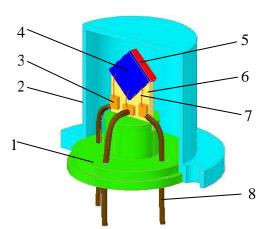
Конструкция герметизированного модуля для регистрации тепловых нейтронов, где 1 — металлическое основание; 2 — металлический корпус; 3 — промежуточный вывод; 4 — ПКД; 5 — гадолиниевый конвертер; 6 — диэлектрический держатель детектора; 7 — перемычка из алюминиевой проволоки; 8 — внешние выводы
